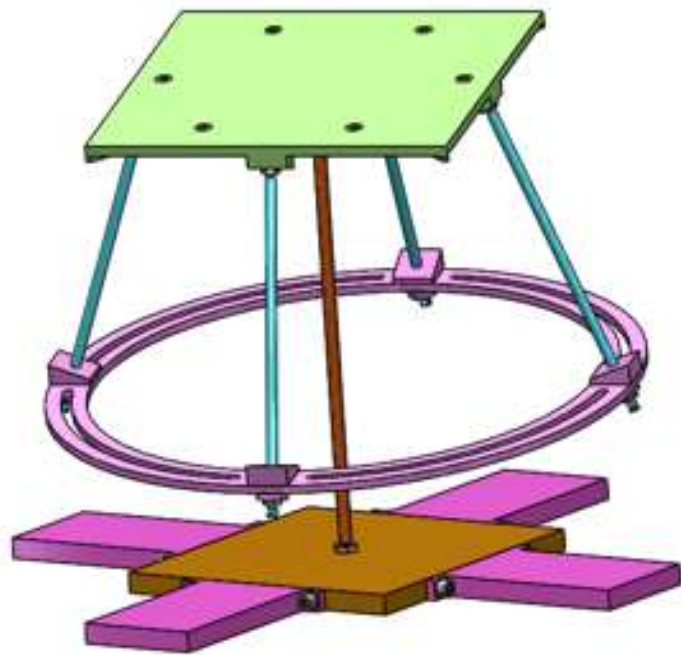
représentation de dessin d'ensemble de la premier modèle
